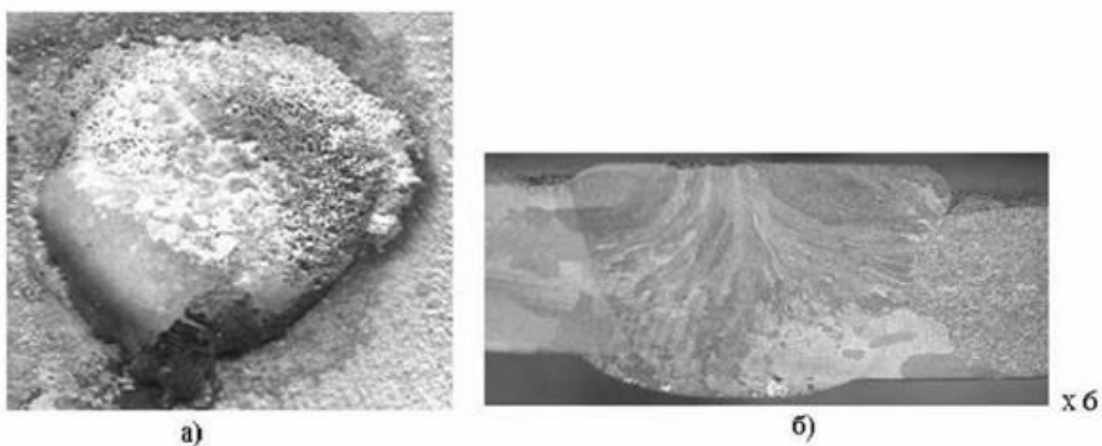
Внешний вид и сечение сварочного кратера при реализации кривой спада тока вида  $y=k(x+b)^{-1}+c$ , выполненного с подачей присадочной проволоки
